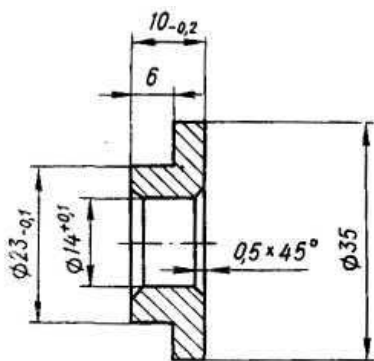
Оправка для запрессовки сальников в картер рулевого механизма
